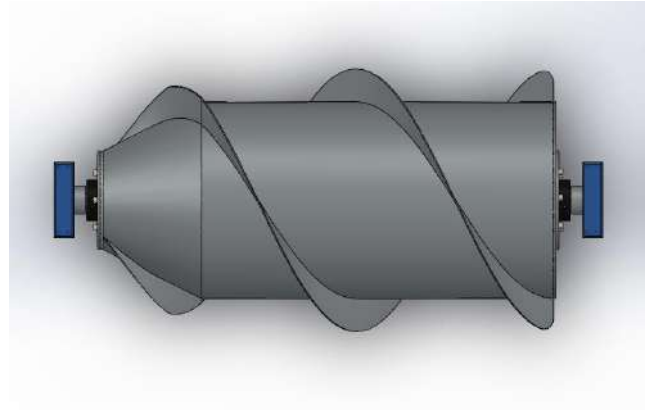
Assembly Bearing pada Housing Bearing
